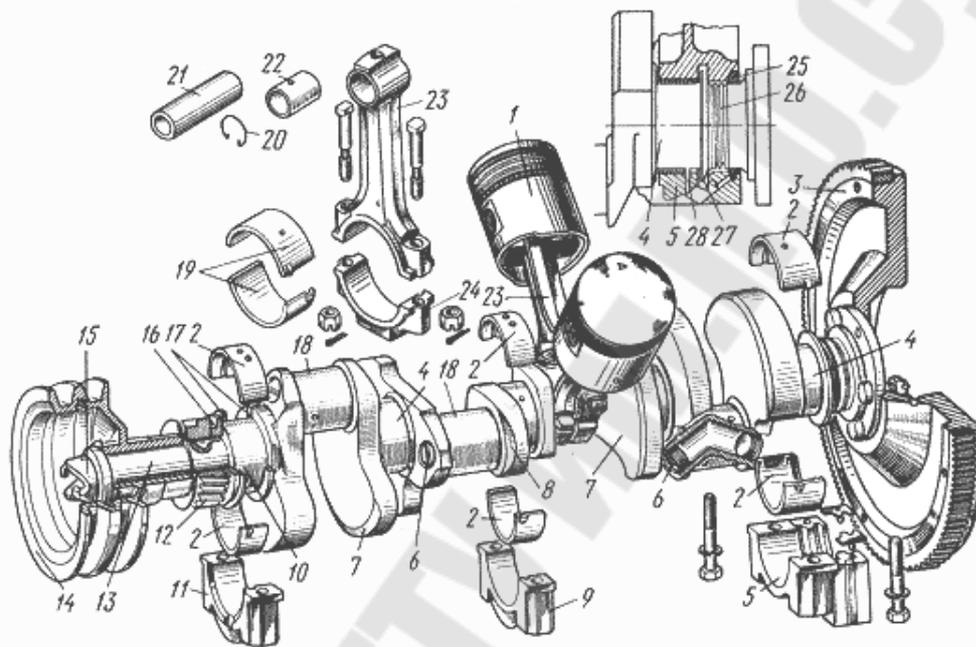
Детали кривошипно–шатунного механизма двигателя ЗИЛ–130:
